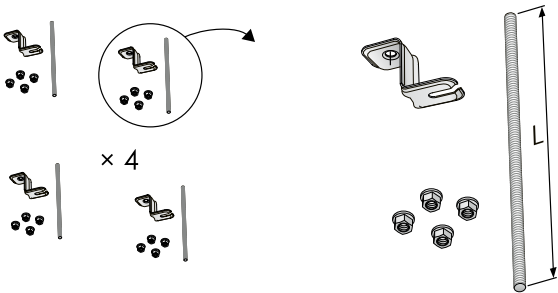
Montageteil SYST MS M8-1, Deckenbefestigung und Gewindestange
